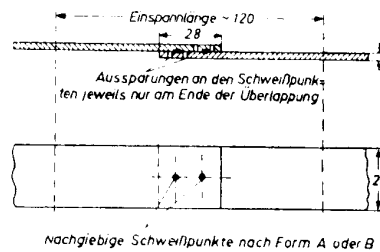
Abmessung und Form der Probe mit nachgiebig ausgeführter Punktschweißung.
